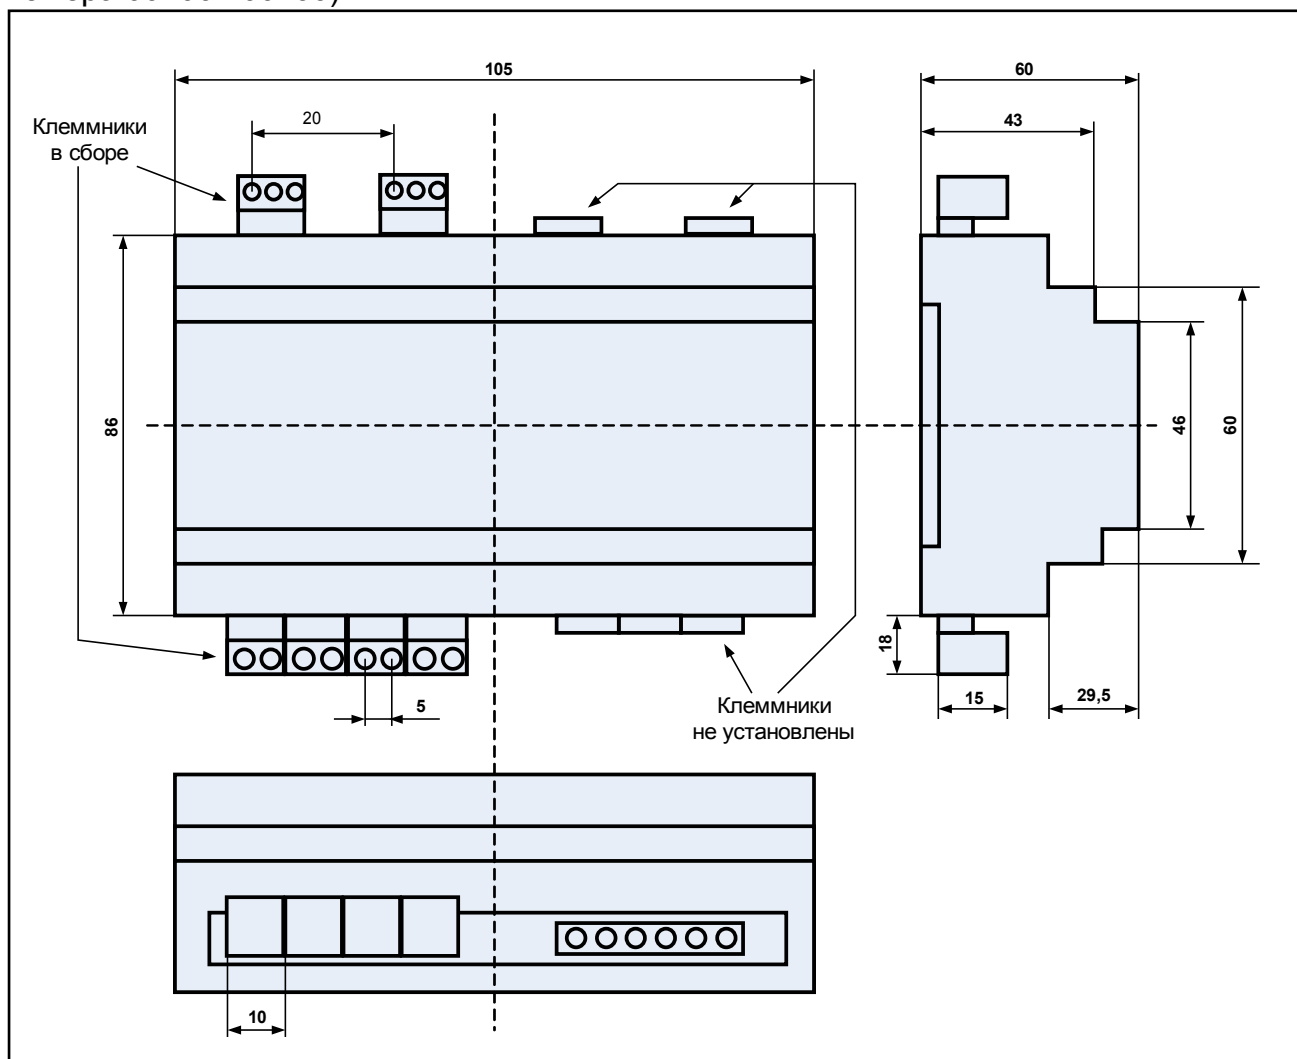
Габаритные размеры корпуса четырехканального устройства (каталожные номера 00400 ...00499)
